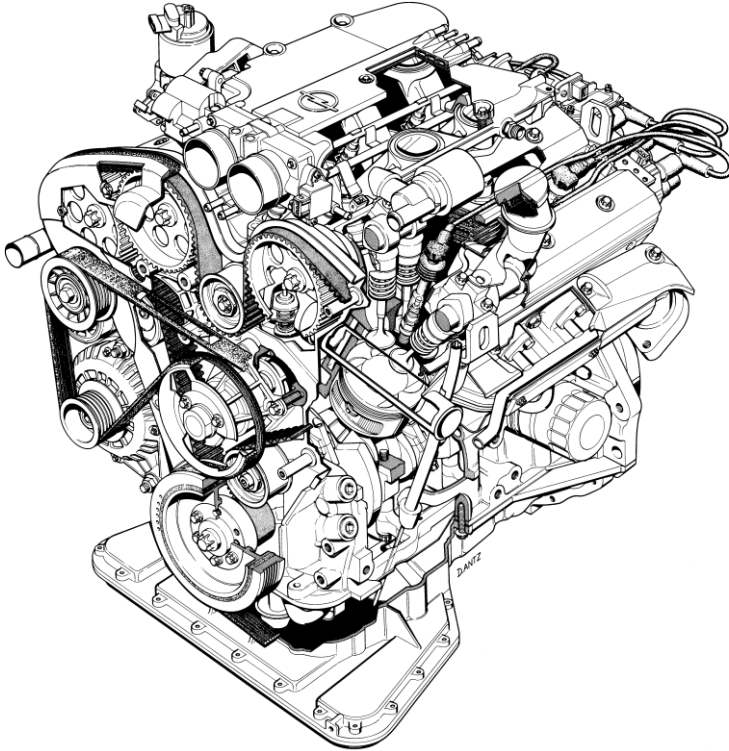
Згальний вигляд звичайного У-подібного двигуна внутрішнього згоряння (фірма Opel).
